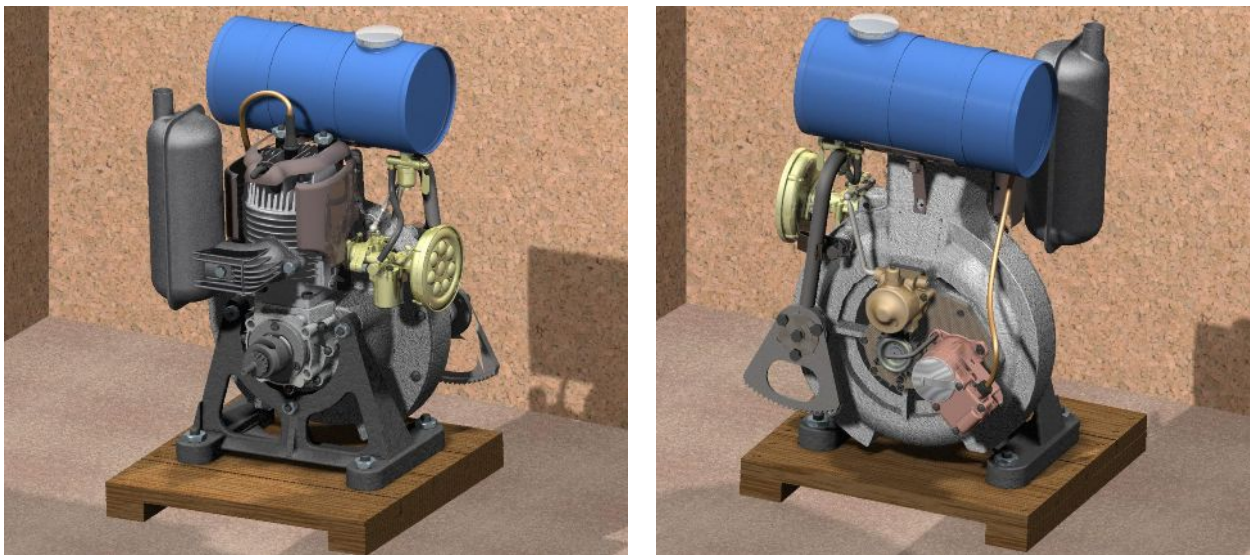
3D-модель двигателя Д300, созданная в SolidWorks
